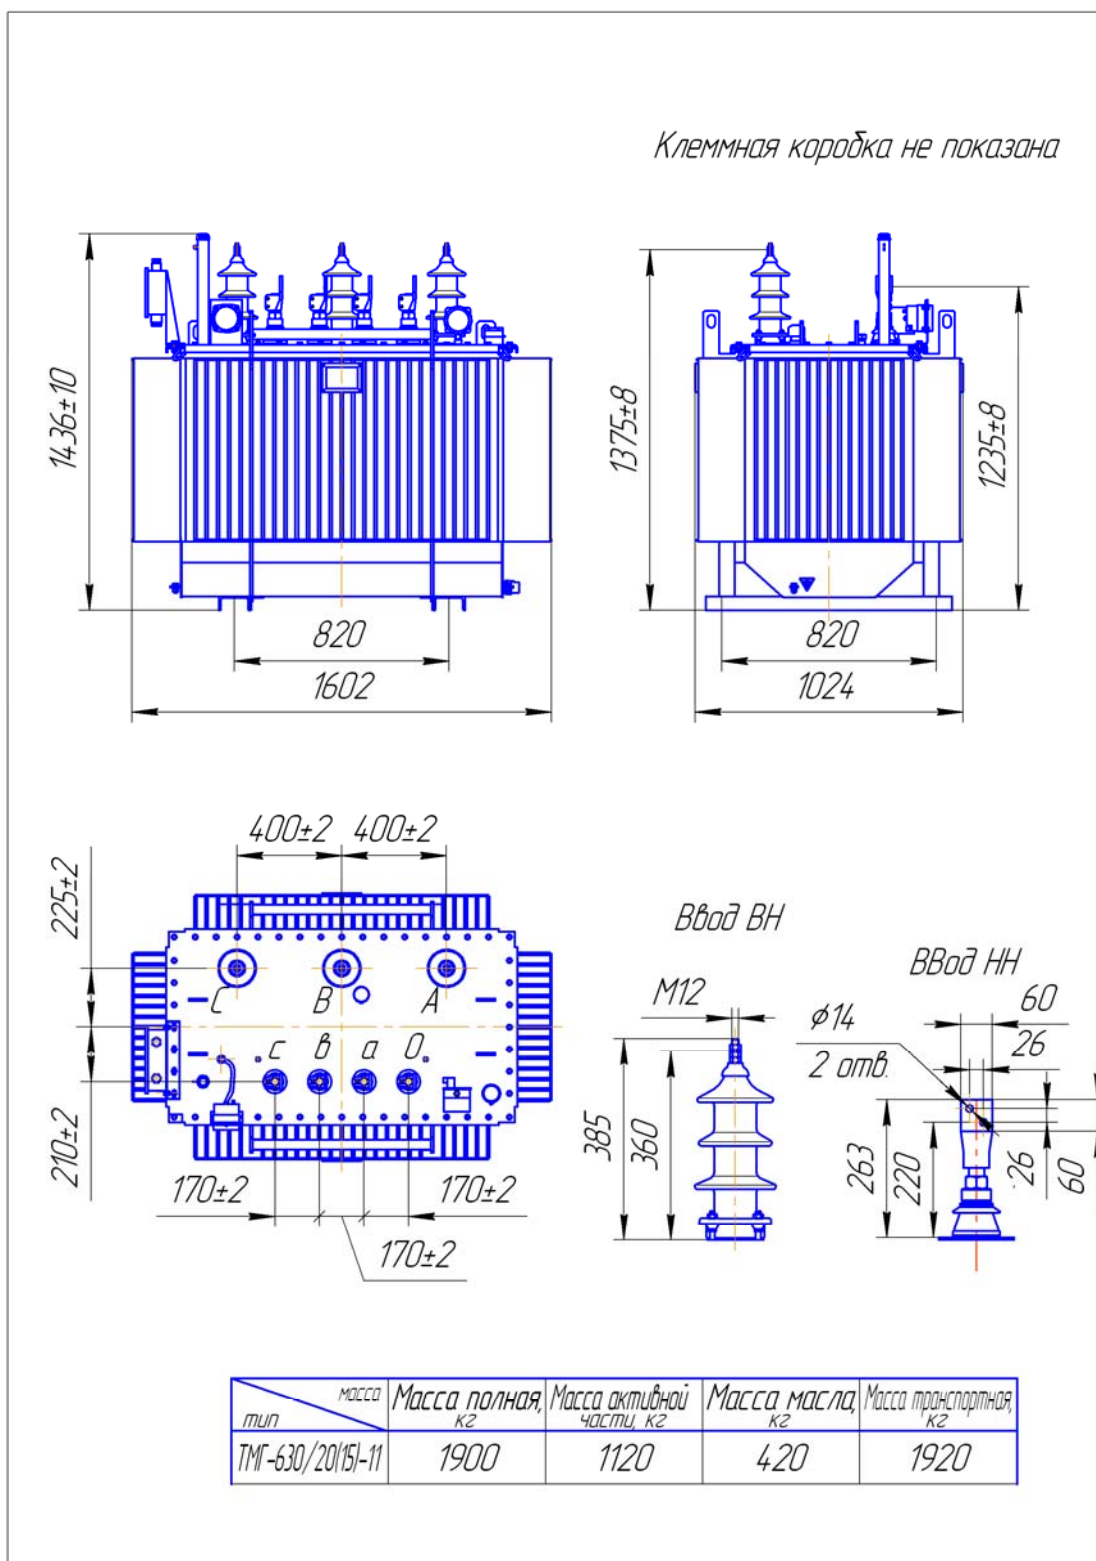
Габаритные, установочные и присоединительные размеры трансформатора ТМГ - 630/20-11
